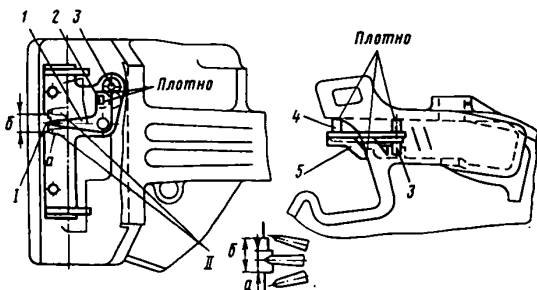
Проверка положения шипа для замкодержателя относительно контура зацепления автосцепки шаблоном 816р
